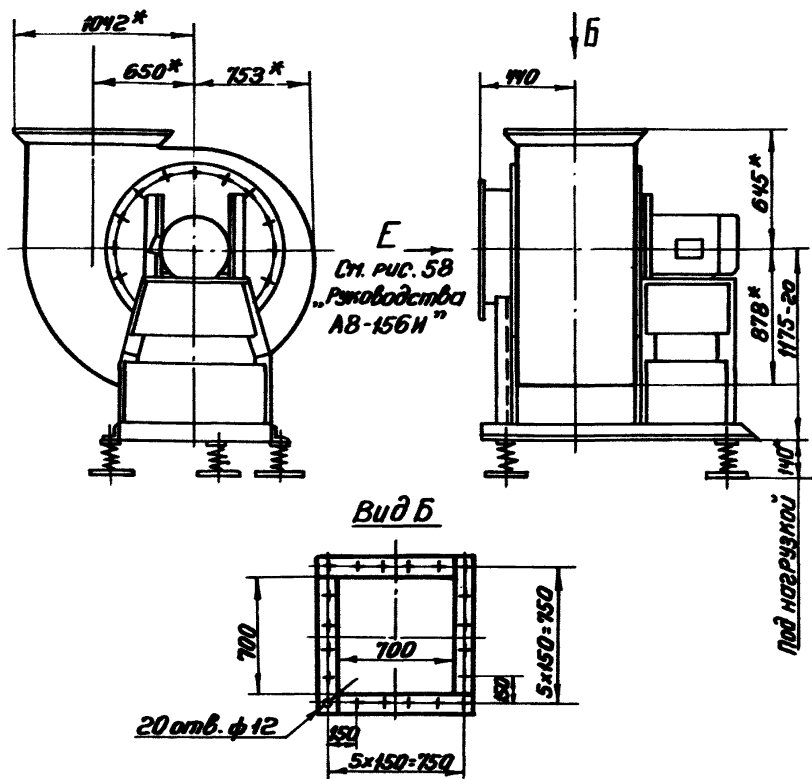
Основные присоединительные и установочные размеры вентиляторов Ц4-70 № 8 (исполнение I)
